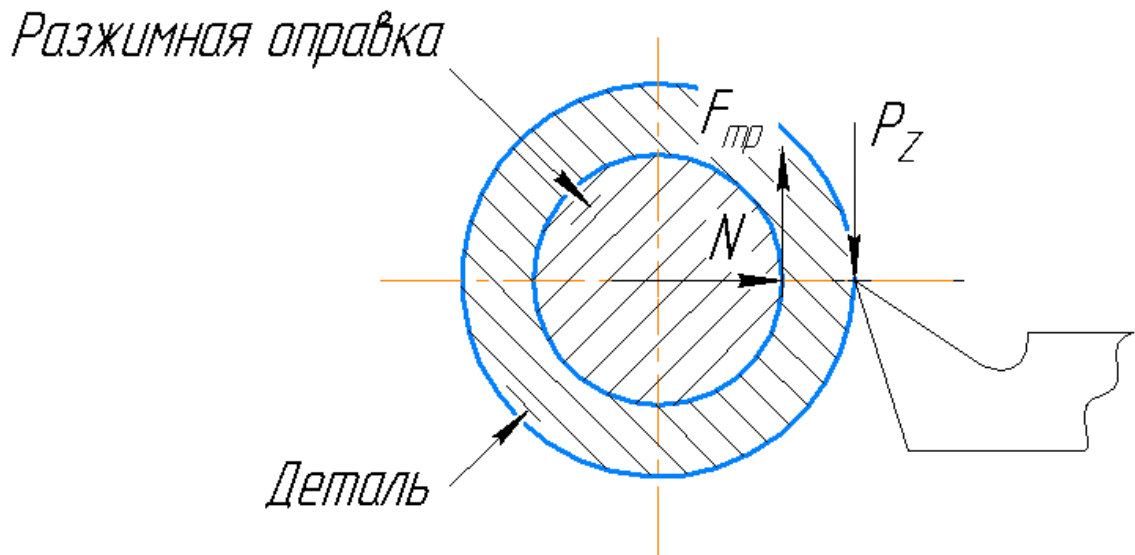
Схема сил, действующих при резании и закреплении заготовки
